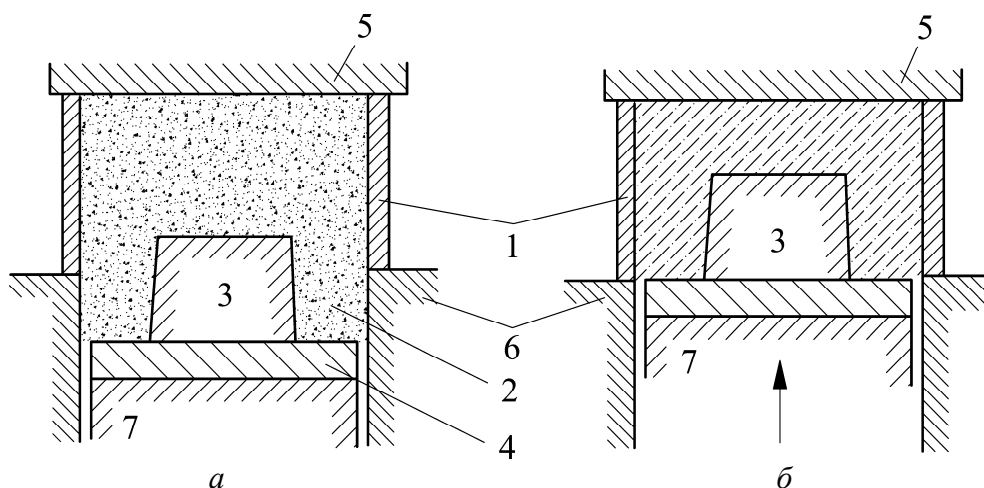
Схема нижнего прессования: *а, б* – до и после прессования; 1 – опока; 2 – наполнительная рамка; 3 – модель; 4 – модельная плита; 5 – неподвижная плита; 6 – неподвижный стол машины; 7 – подвижный прессовый стол машины
